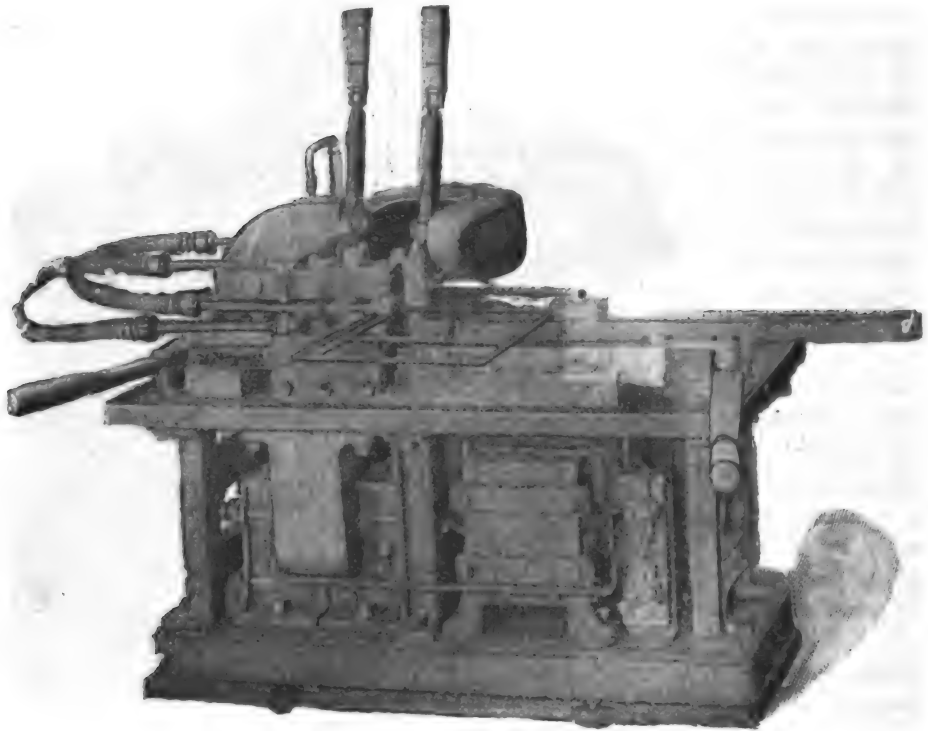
Machine à souder pour faire des soudures de pièces à angle droit.
